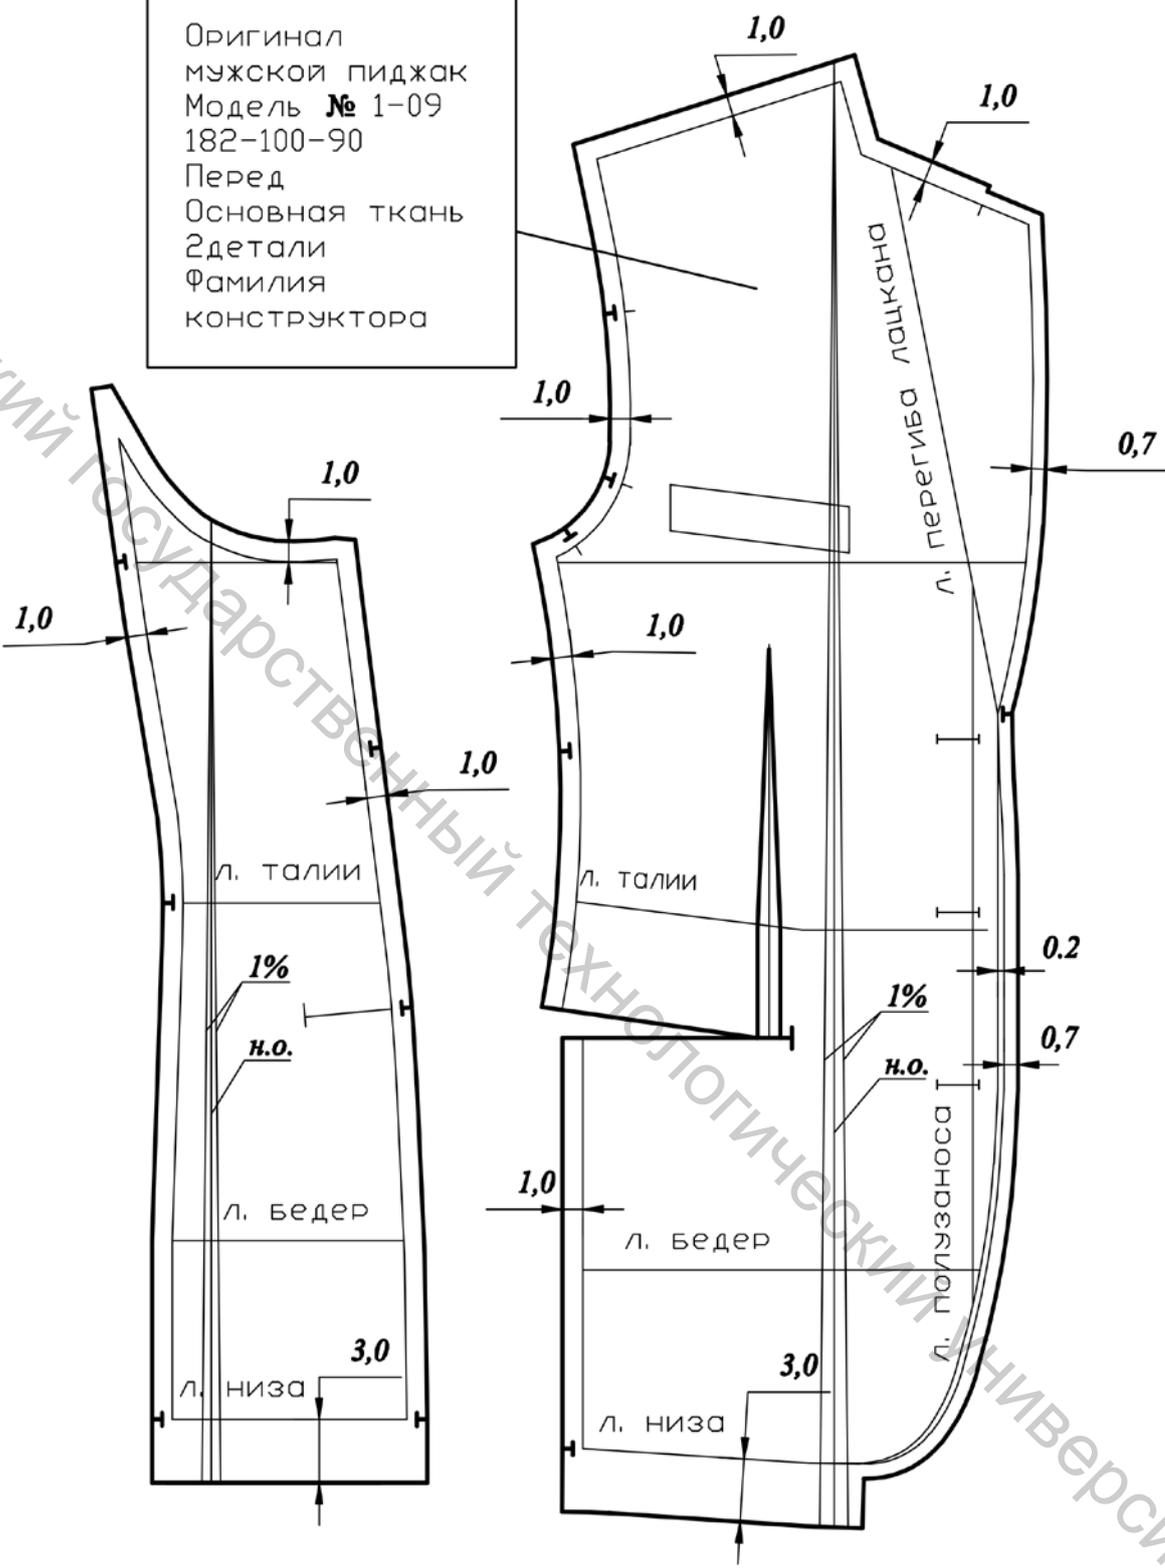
Чертежи лекал основных деталей мужского пиджака (перед, бочок)
